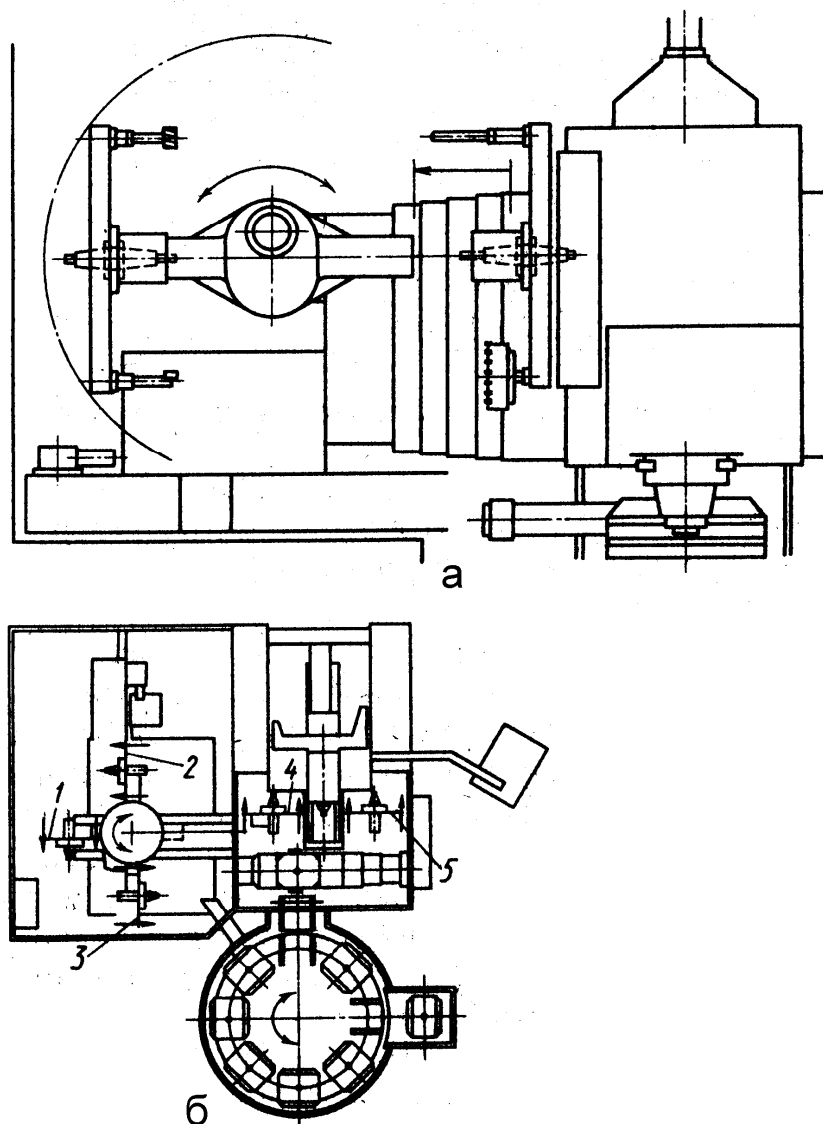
ГВМ фірми «Хюллер Хіллі» з резервними інструментальними магазинами: а – автоматична заміна інструментальних дисків; б – гнучкий осередок з двома робочими і трьома резервними інструментальними дисками
